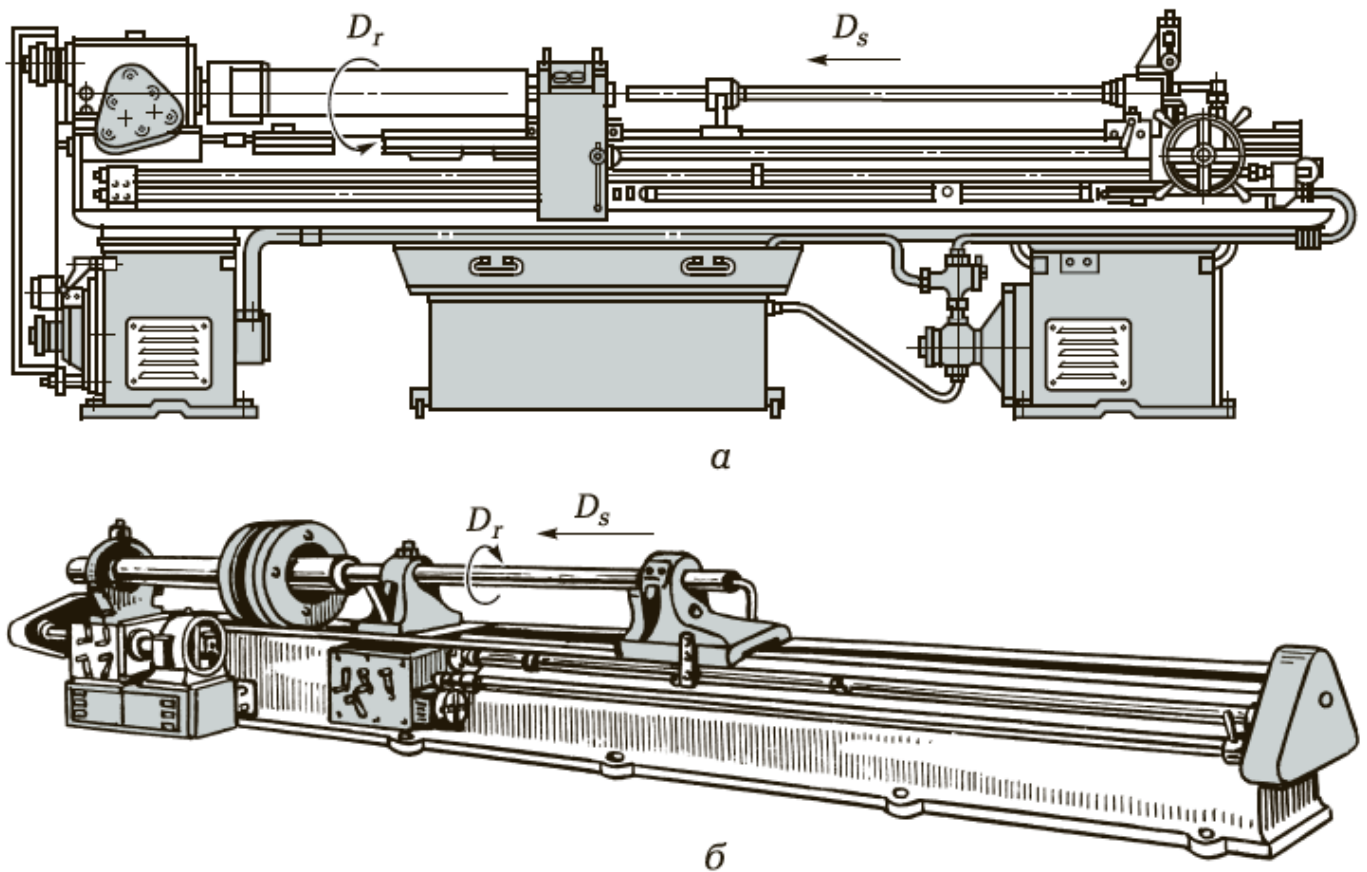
Горизонтально-сверлильные станки для глубокого сверления вращающихся заготовок (а) и (б):
